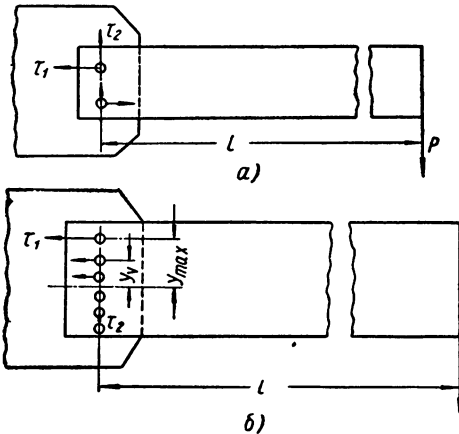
Двухсрезное соединение с накладками при точечной сварке.
